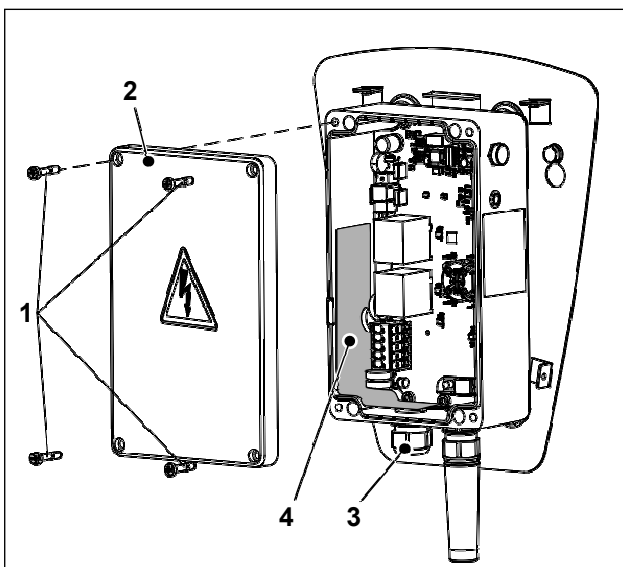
EVC-W1-ECO5M Wallbox, caja del aparato electrónico abierta
